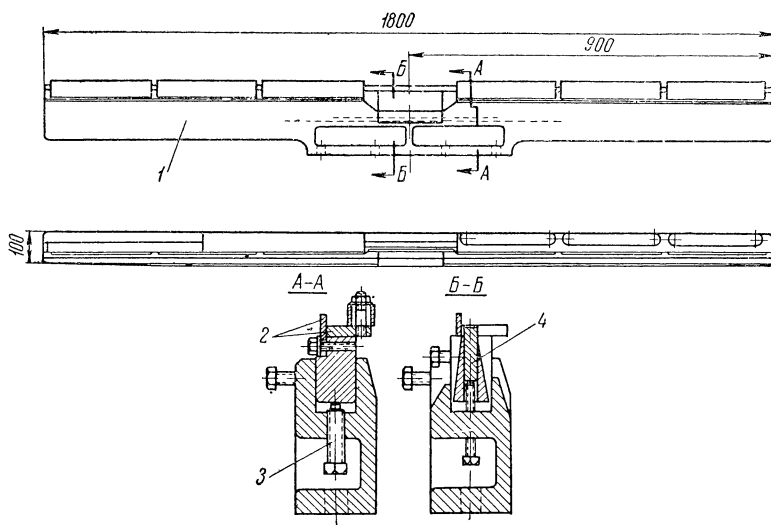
Приспособление для бесцентрового шлифования длинных осей.
